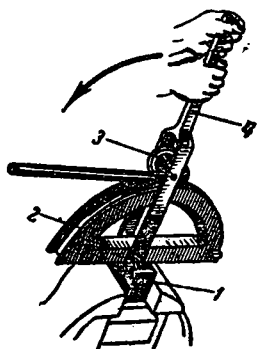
Ручное приспособление для гибки труб с одним роликом для обкатки
